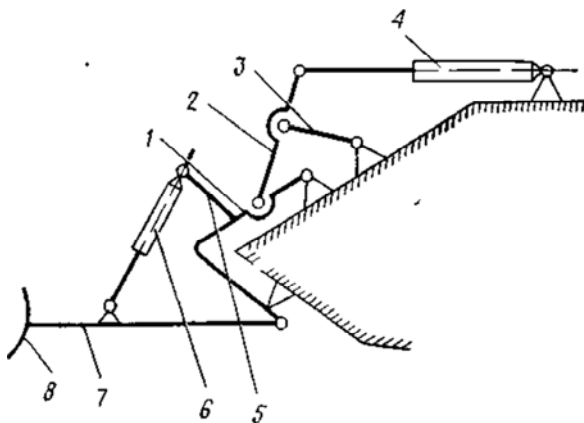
Схема механизмов управления универсальным бульдозерным оборудованием: 1 – подъемная рама; 2 – коромысло; 3 – кривошип; 4 – гидроцилиндр механизма перевода; 5 – Г-образный кронштейн; 6 – гидроцилиндр заглибления; 7 – толкающая рама; 8 – отвал
